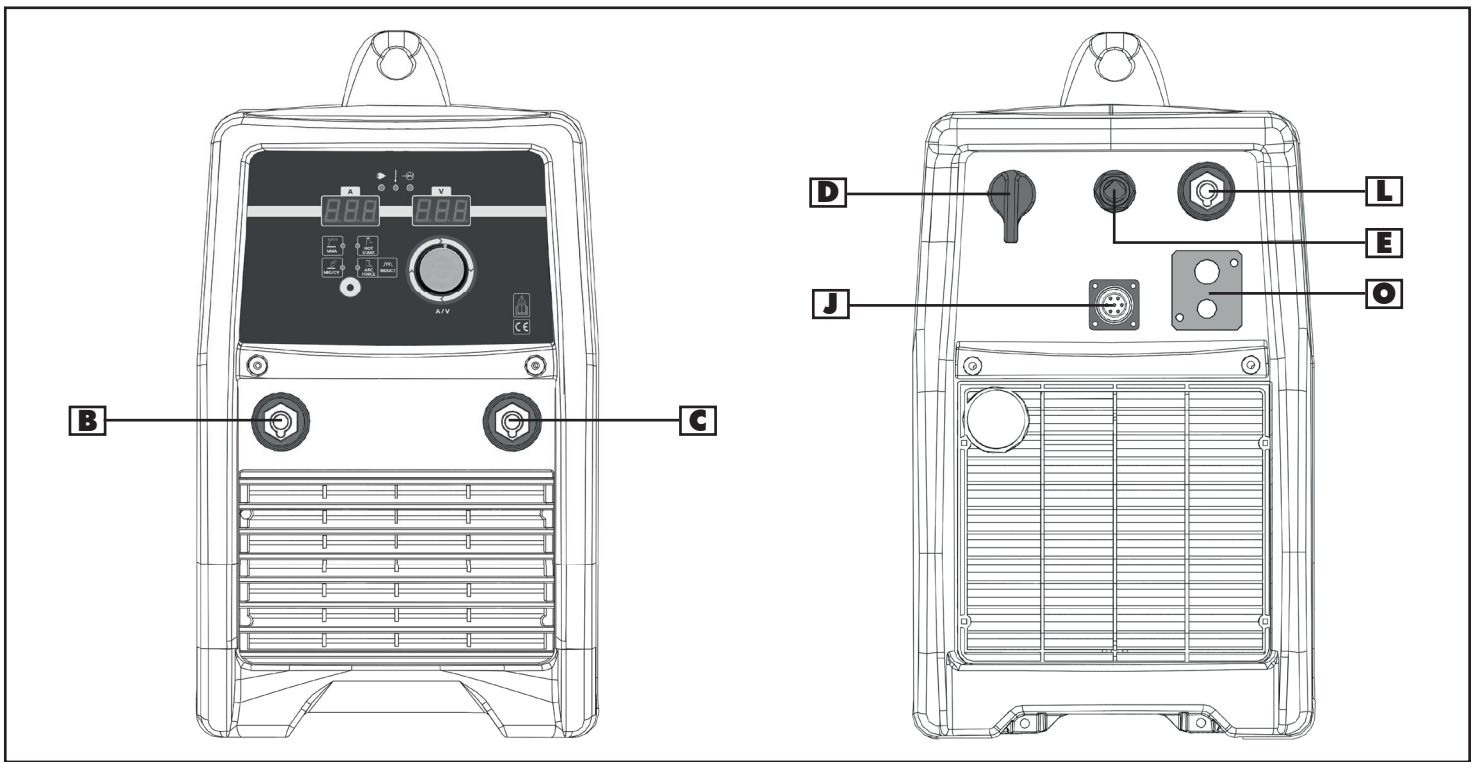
Unitech 418-558: Générateur - vue avant et arrière
